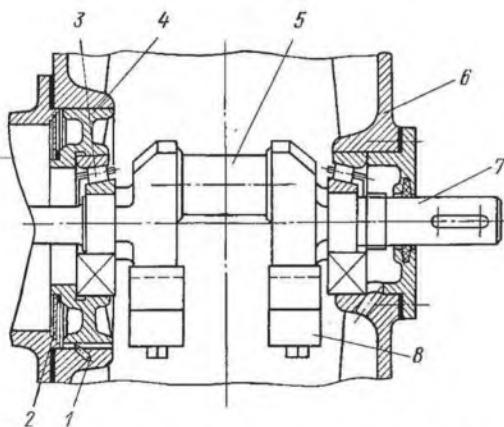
Двухопорный коленчатый вал на конических подшипниках:
